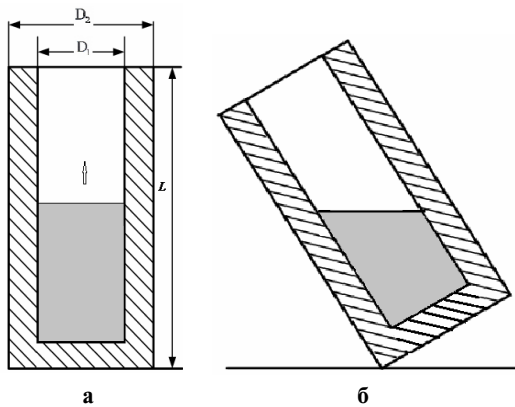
Схема заповнення рідиною пружно-пластичного циліндричного тіла: а – циліндр заповнюється рідиною (розплавом металу); б – циліндричне тіло заповнюється рідиною під кутом
